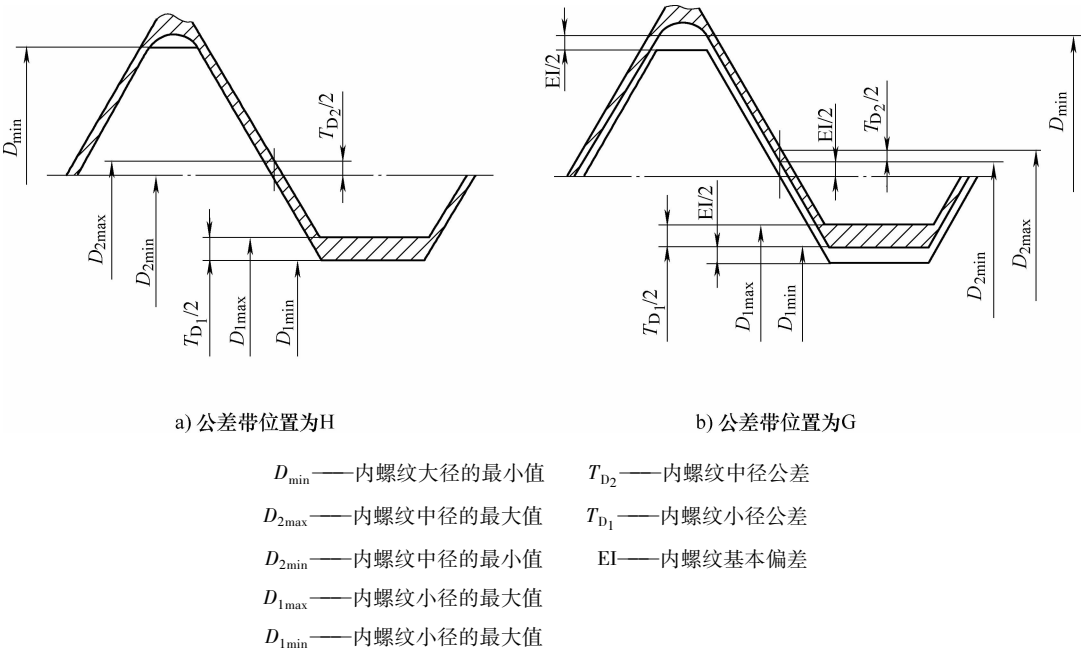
普通内螺纹公差带及其各直径位置
